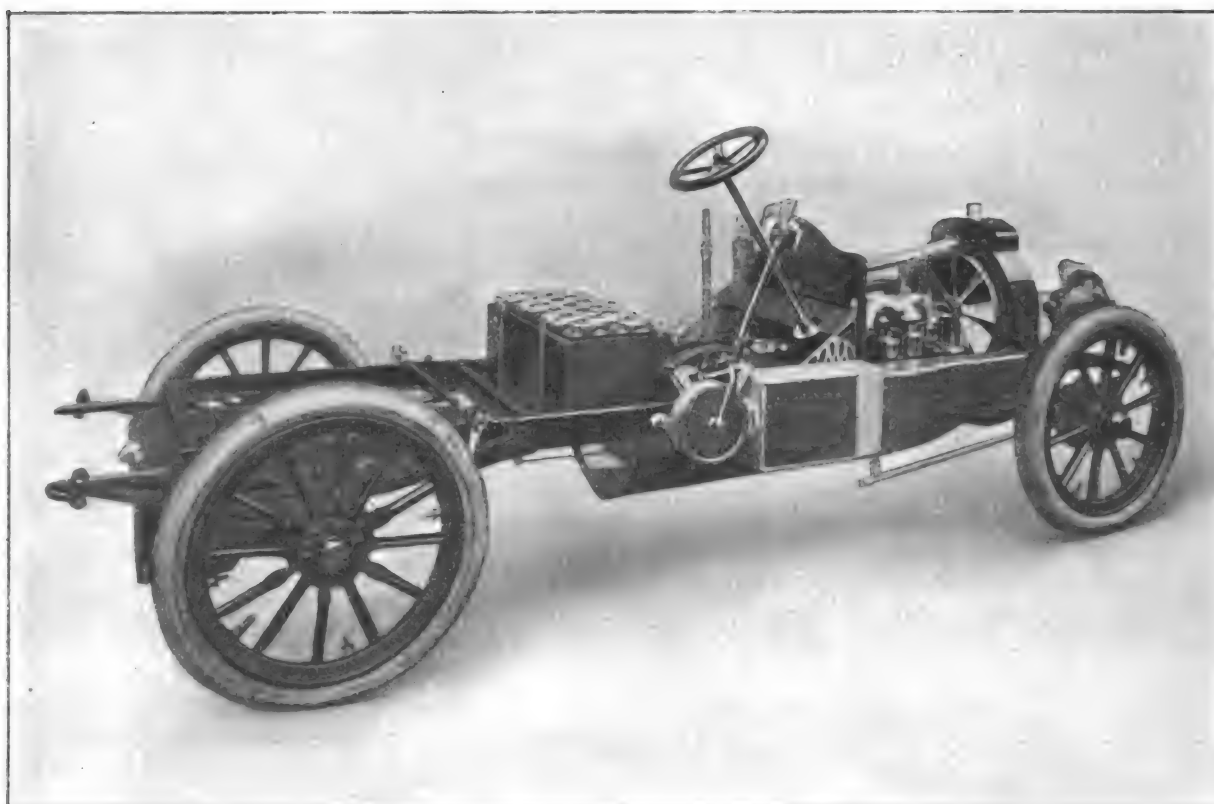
Vue d'ensemble du châssis de l'Auto-mixte.
